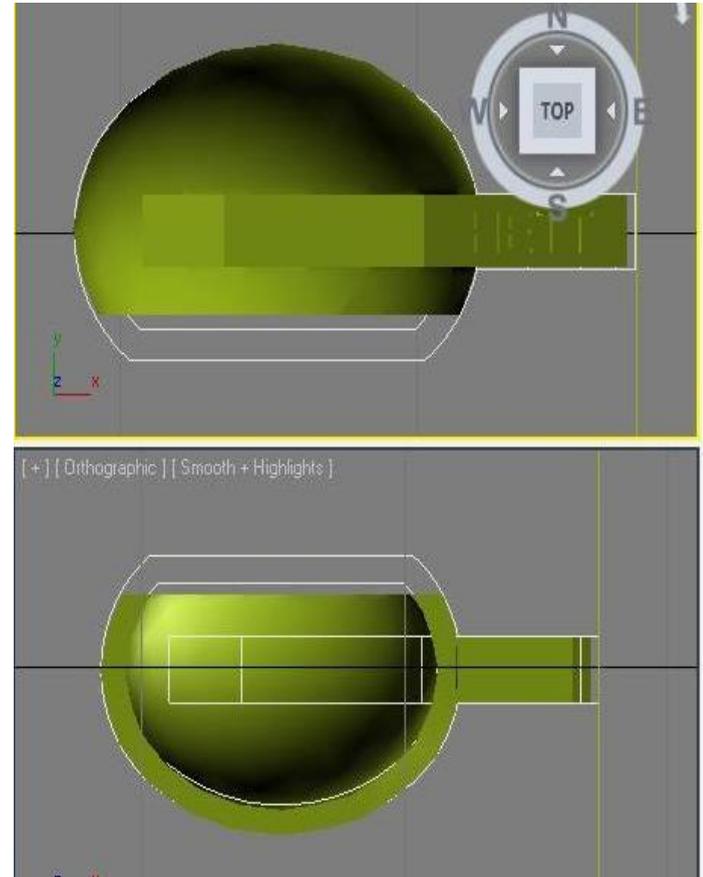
modelado de rodete, vista en planta superior e inferior
